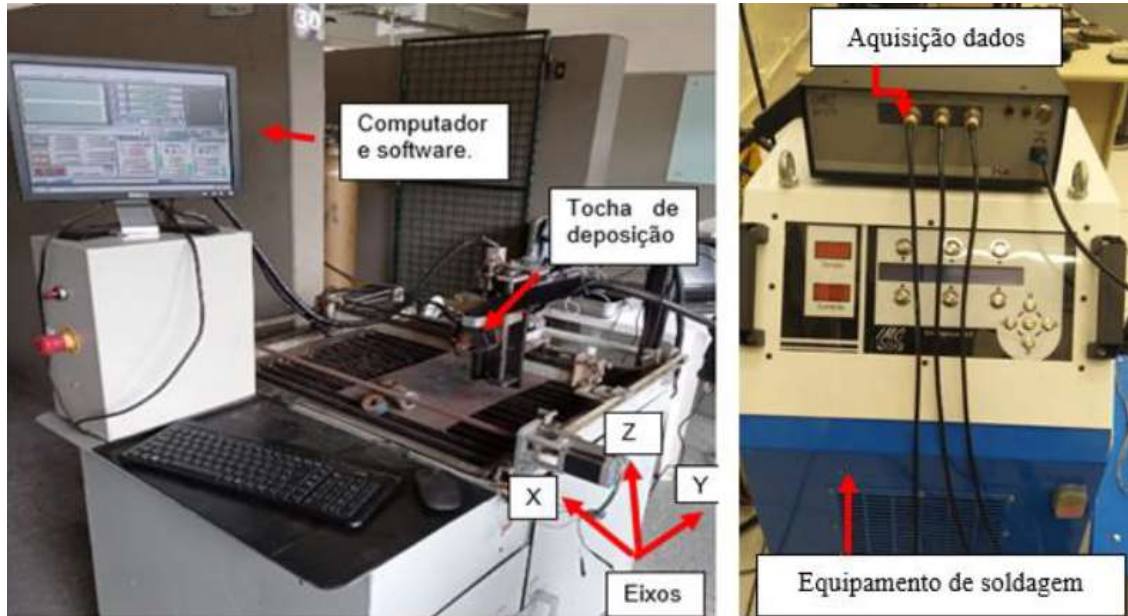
Equipamento CNC para impressão 3D. máquina de soldagem IMC DIGplus A7 e, ferramentas para aquisição de dados de soldagem.
